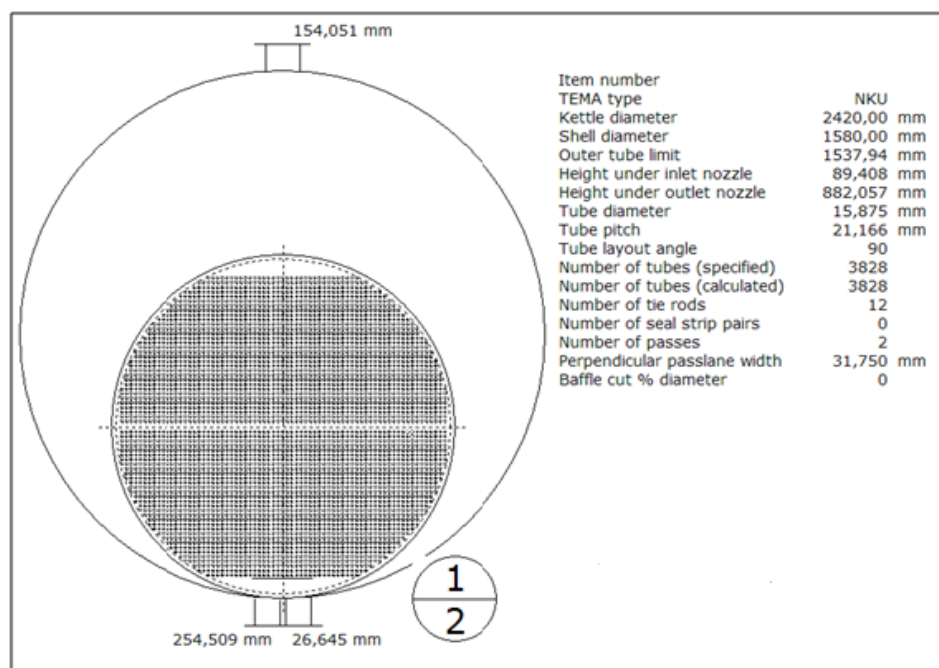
Huella de tubos del Kettle Fuente: HTRI layout
